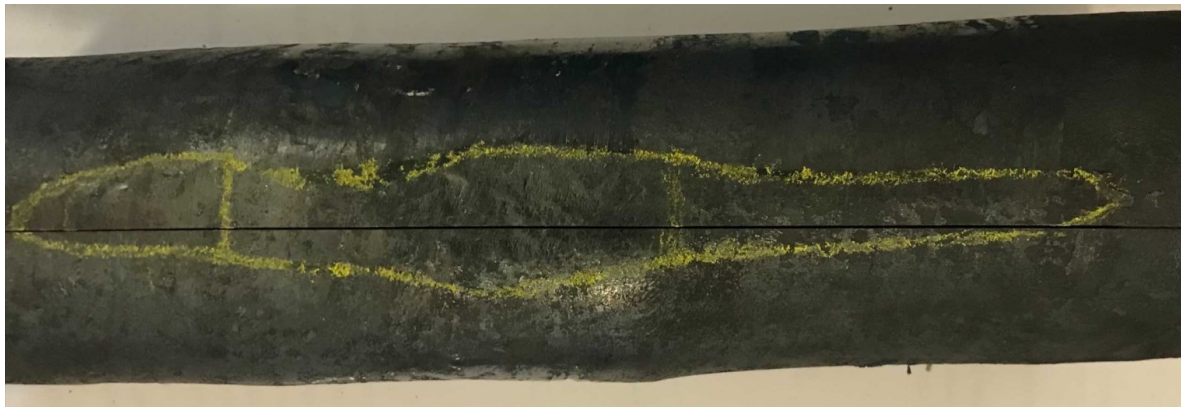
Заторможенный образец гильзы-трубы в процессе раскатки
